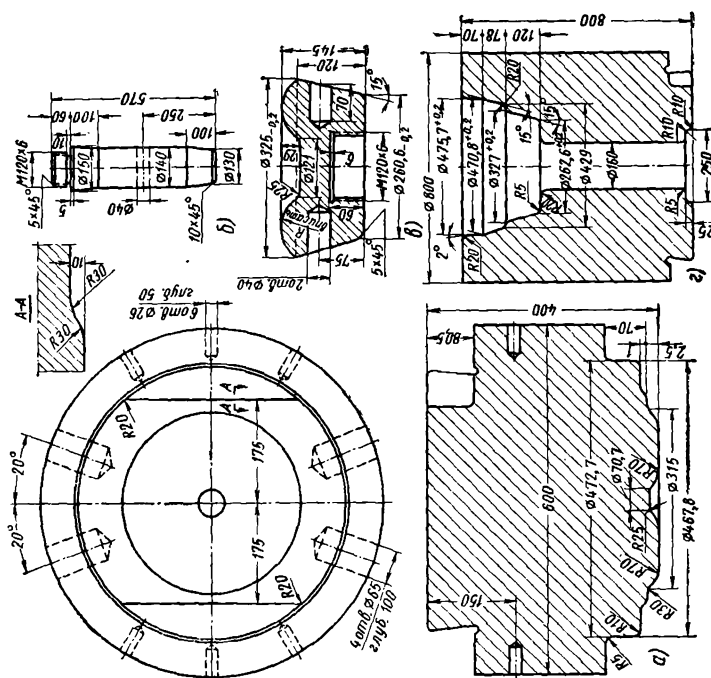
Детали штампа для штамповки дисков: а — разгонка; б — толкатель; в — выталкиватель; г — нижний штамп
